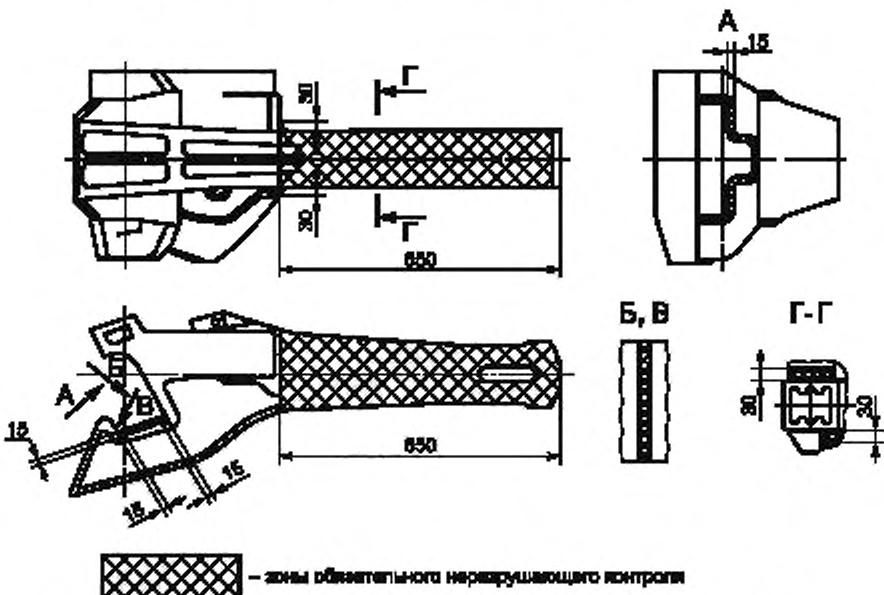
б) — Зоны неразрушающего контроля на корпусах автосцепок СА-3М
